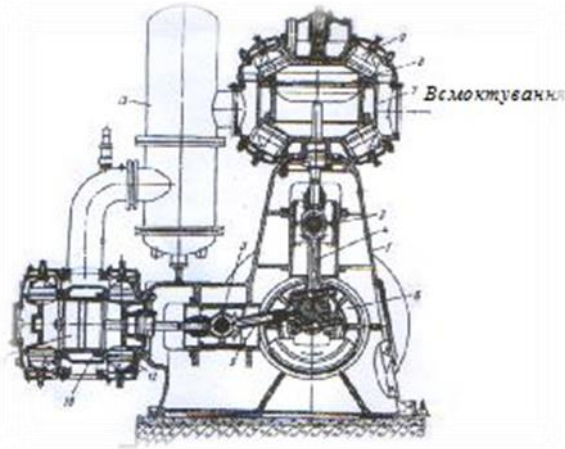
Поршневий компресор 305ВП-30/8
